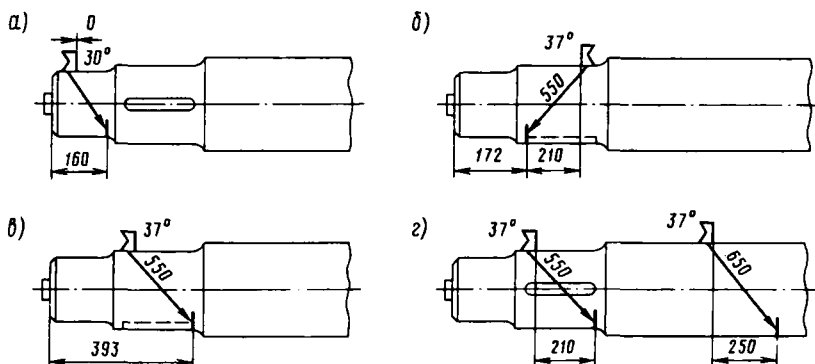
Схемы и зоны контроля главного приводного вала эскалатора ЛТ-4 наклонными искателями в галтелях (а, в) и в шпоночной канавке (б, г)
